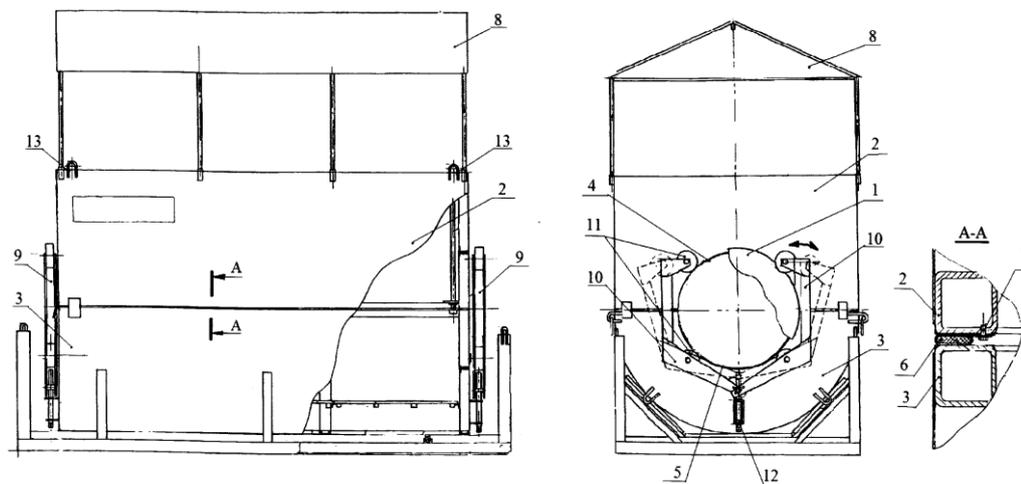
Конструкция герметичной камеры. 1 – трубопровод; 2 – корпус; 3 – днище; 4, 5 – арочные вырезы; 6 – уплотнительный элемент; 7 – болт; 8 - крыша; 9 – захват; 10 – захватный элемент; 11 – ролики; 12 – регулировочный винт; 13 – монтажные петли
